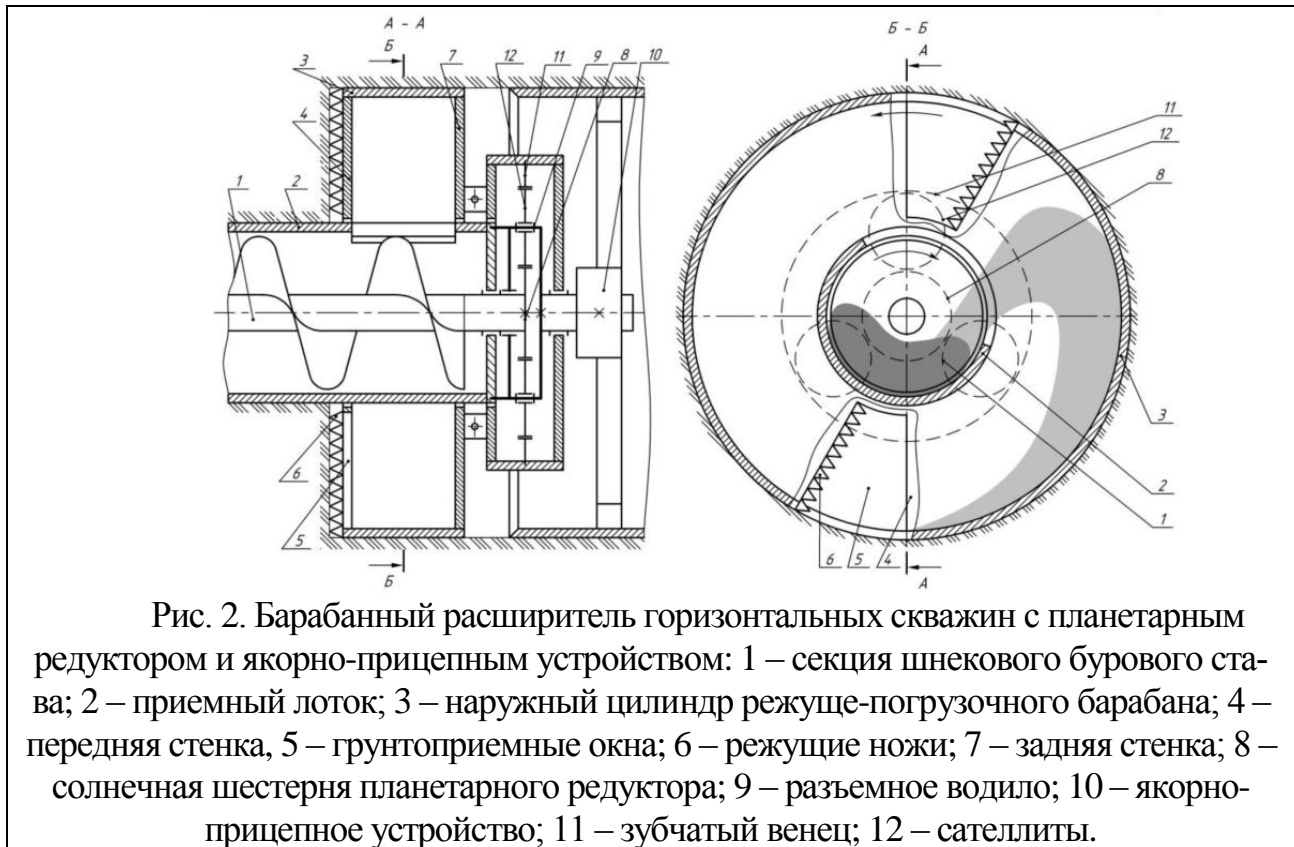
Барабанный расширитель горизонтальных скважин с планетарным редуктором и якорно-прицепным устройством: 1 – секция шнекового бурового става; 2 – приемный лоток; 3 – наружный цилиндр режуще-погрузочного барабана; 4 – передняя стенка; 5 – грунтоприемные окна; 6 – режущие ножи; 7 – задняя стенка; 8 – солнечная шестерня планетарного редуктора; 9 – разъемное водило; 10 – якорно-прицепное устройство; 11 – зубчатый венец; 12 – сателлиты.
